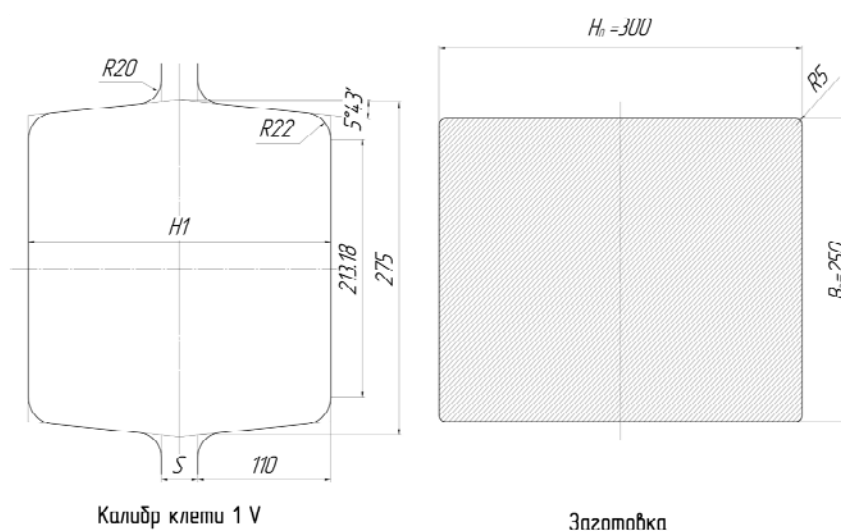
Геометрия калибра клетки № 1V черновой группы стана 370/150 и размеры непрерывнолитой заготовки: H_1 – изменяемая высота полосы, мм; S – изменяемый межвалковый зазор, мм
